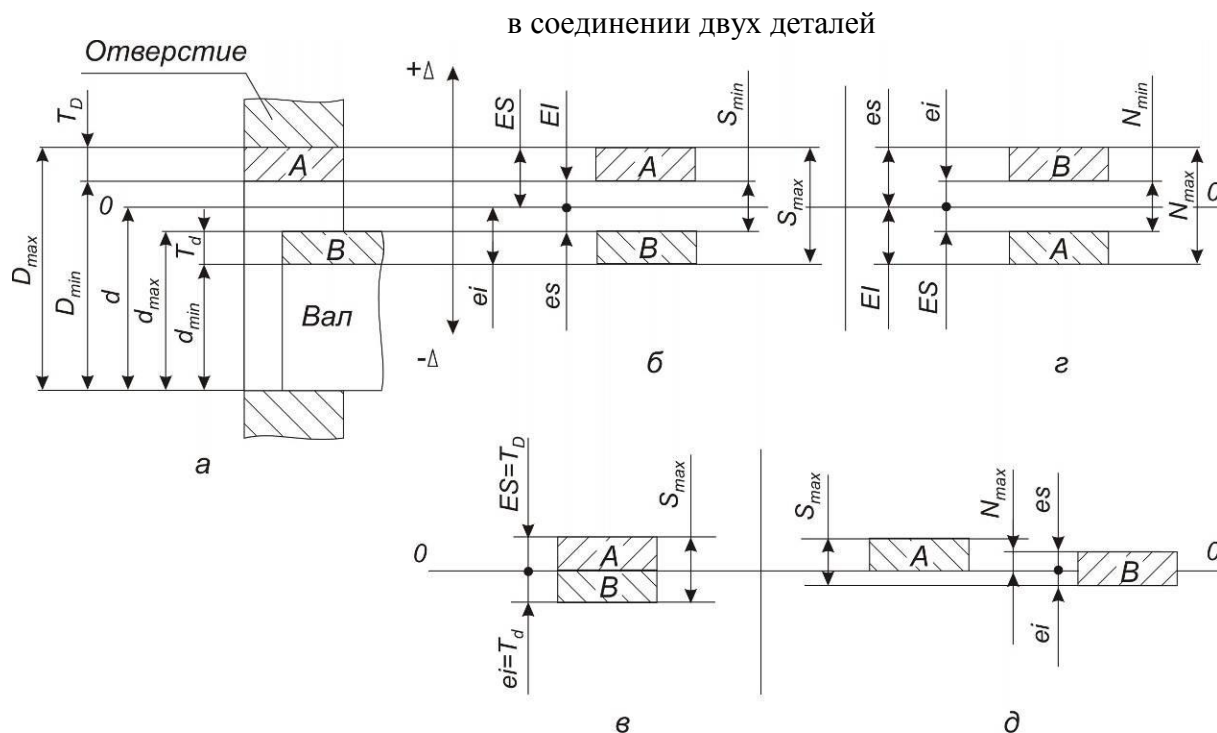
Расположение полей допусков отверстия *A* и вала *B*:
